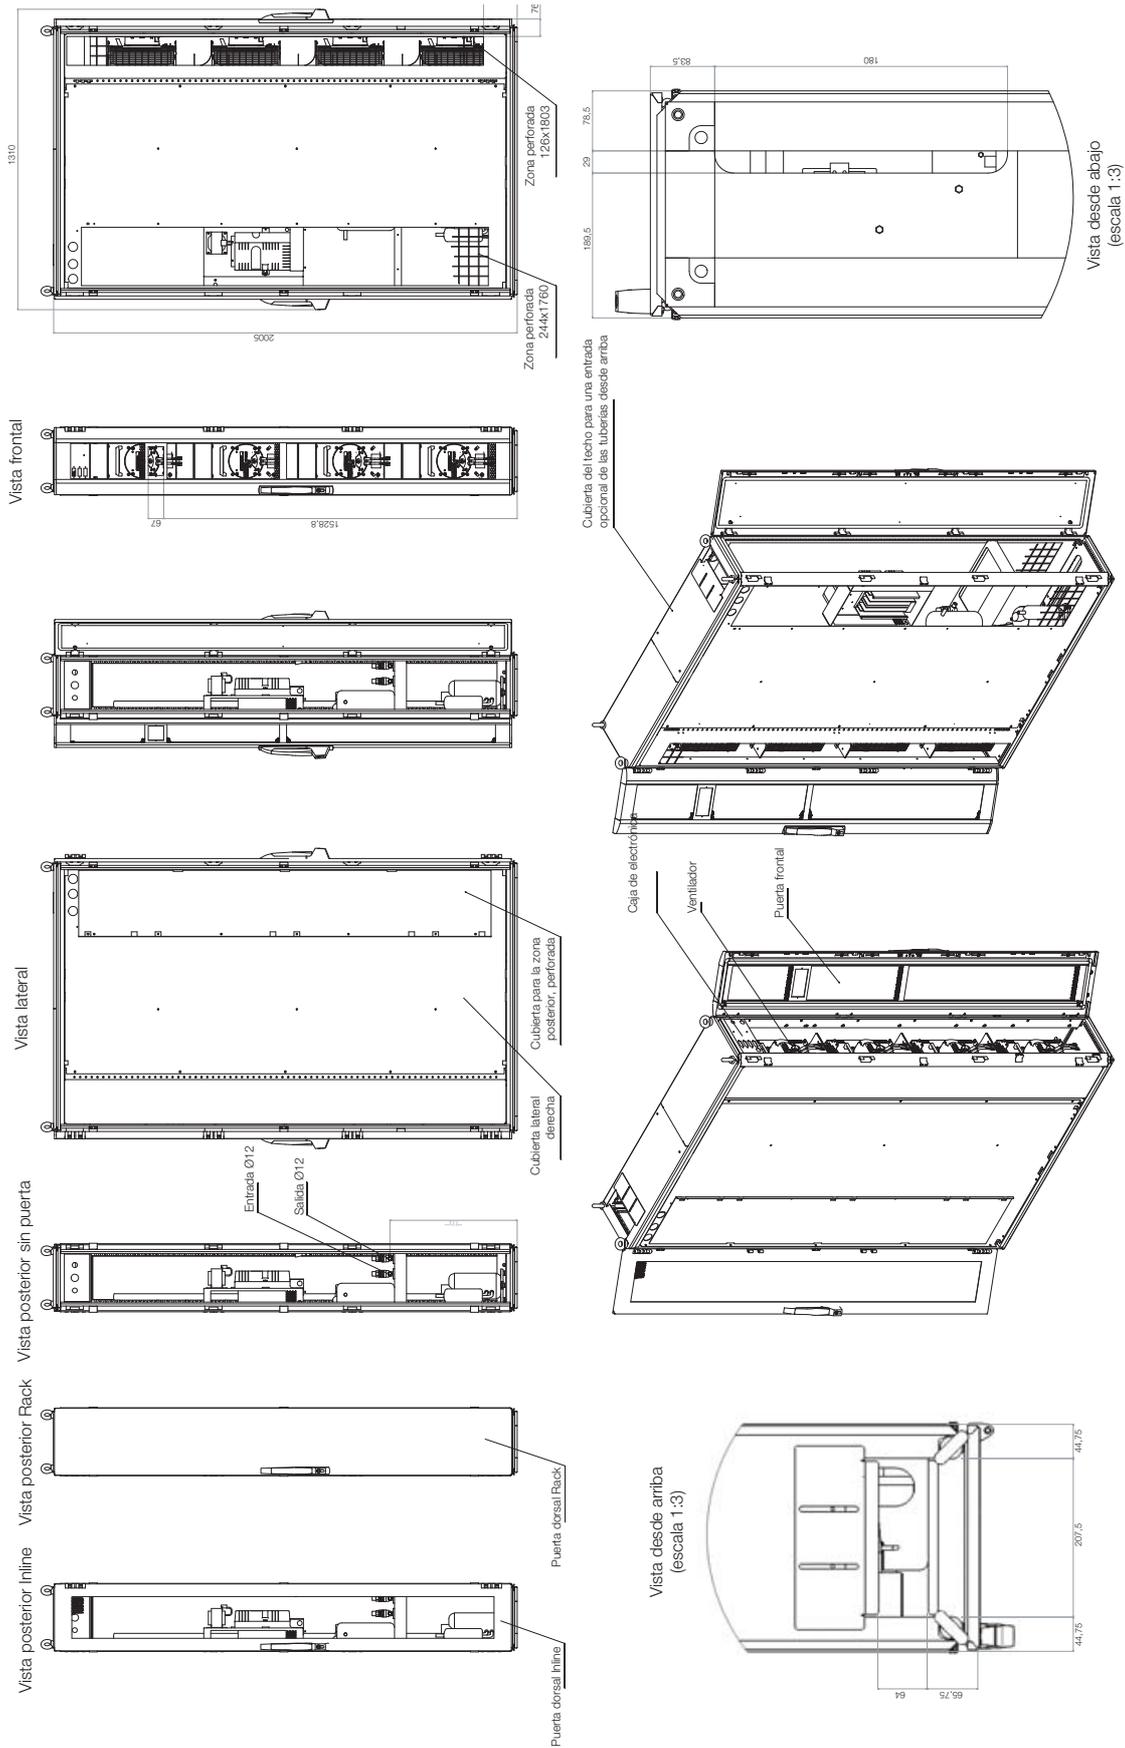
Plano de conjunto LCP DX (1200 mm prof.)
